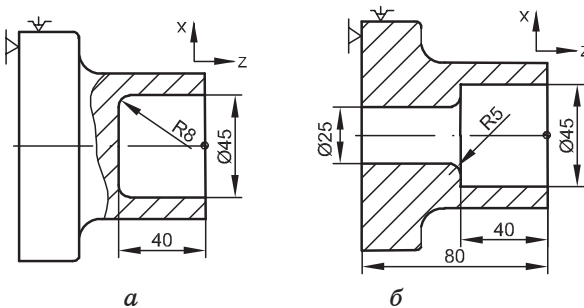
Обробка на внутрішній поверхні деталі: а — галтелі; б — заокруглення
